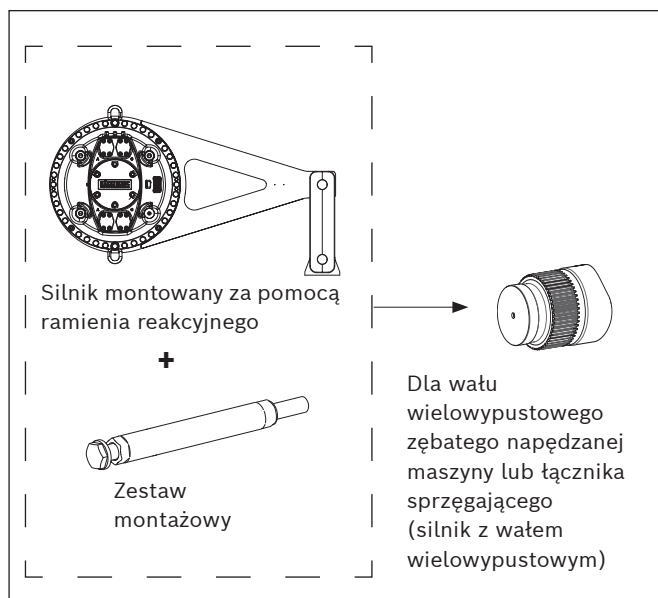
Montaż dwustronnego ramienia reakcyjnego DTCB 0400 do DTCB 1120 dla CB 280 do CB 1120
